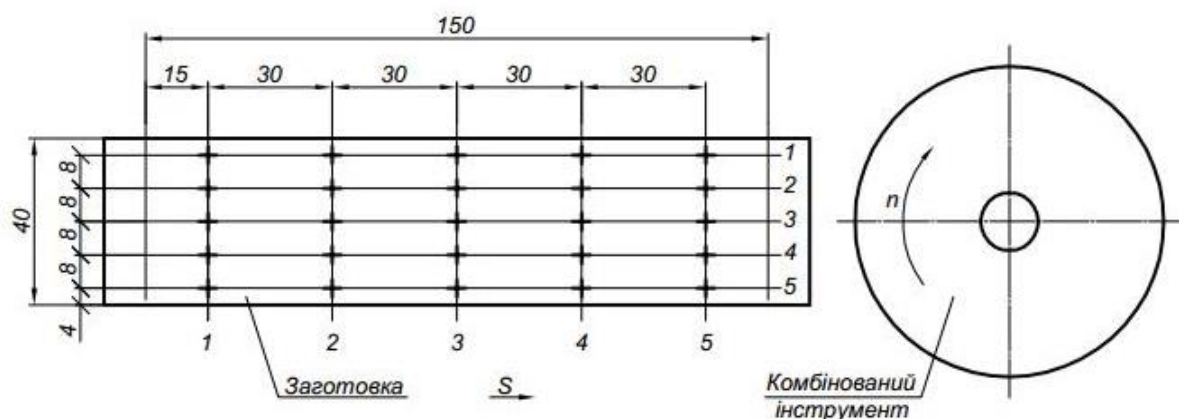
Схема вимірювання шорсткості обробленої поверхні
